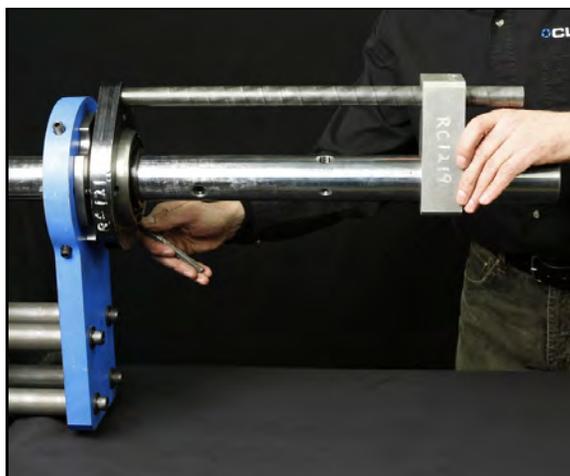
HERRAMIENTA DE ALINEACIÓN SOBRE LA VARILLA DE MONTAJE
